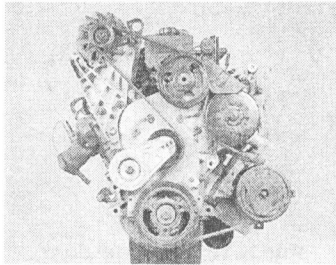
а. Двигатель 3, 1 л – вид со стороны приводного ремня.
